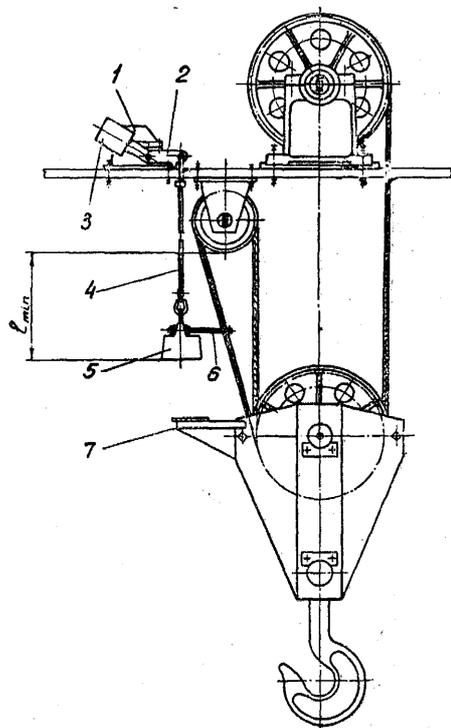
Установка конечного выключателя механизма подъема груза.
